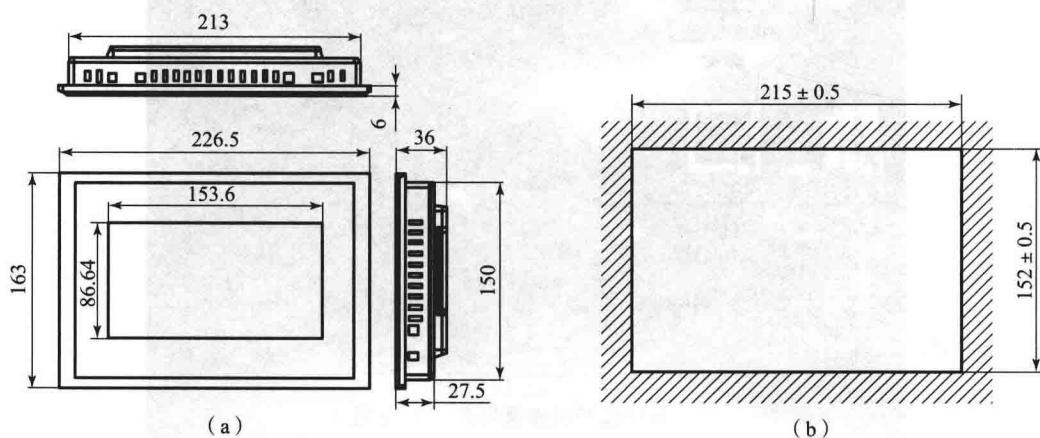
14 TPC7062 产品的外形尺寸及安装的开孔尺寸
